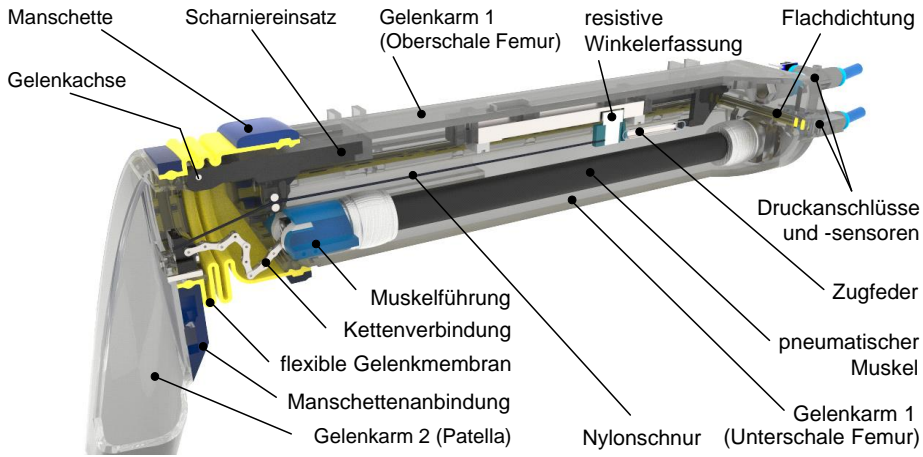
Technisch ausgereifter Prototyp des bionischen Spinnenbeingelenkes.
